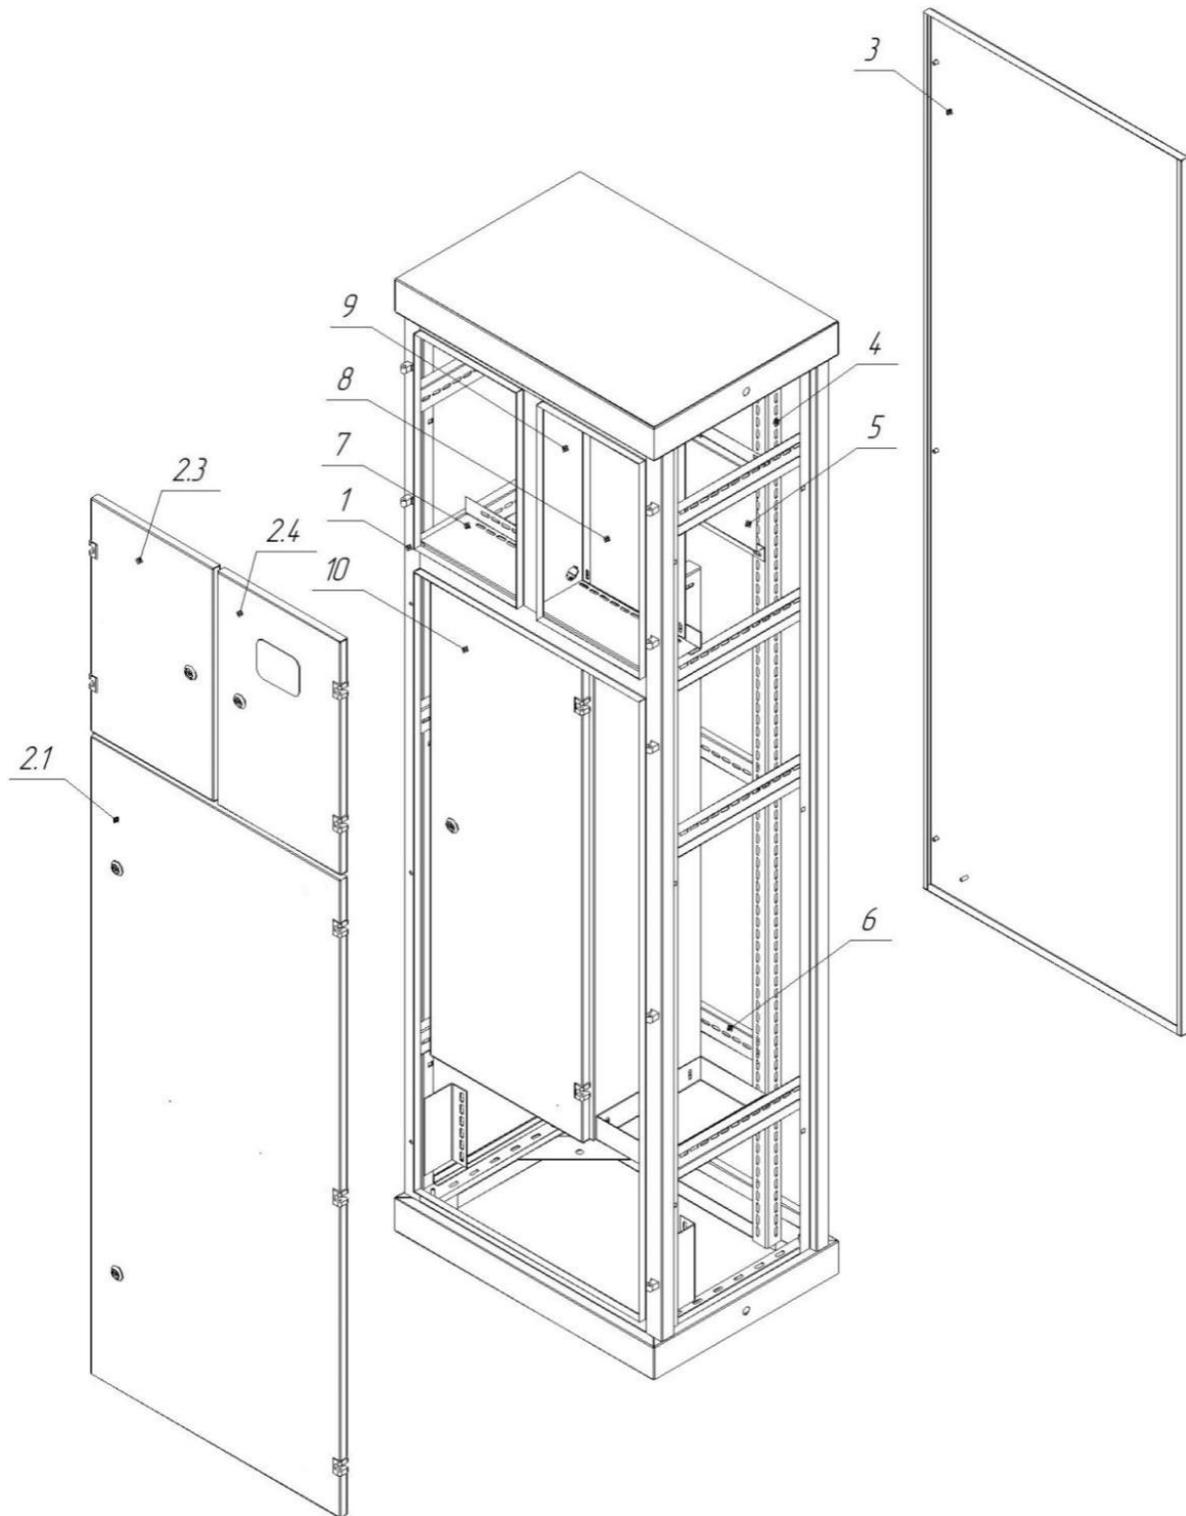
Устройство металлокорпуса ВРУ-3 с отсеком рубильника
